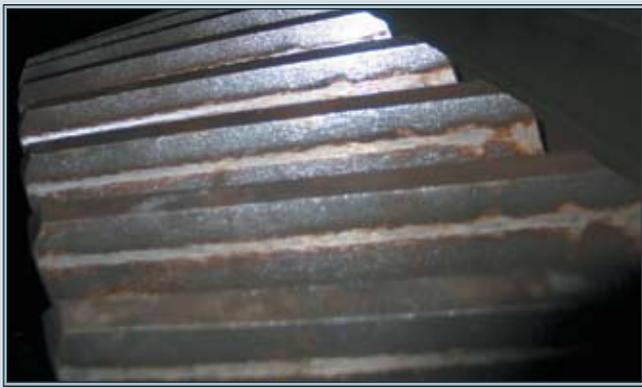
Пятно контакта на нерабочей поверхности зуба колеса
